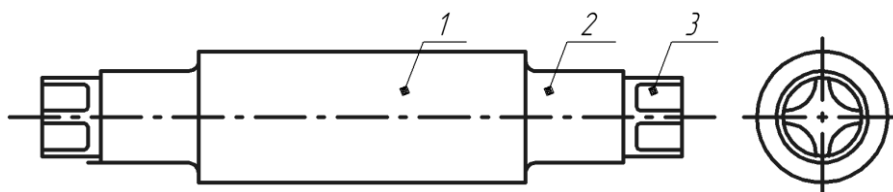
Типовая конструкция рабочего валка прокатного стана:
